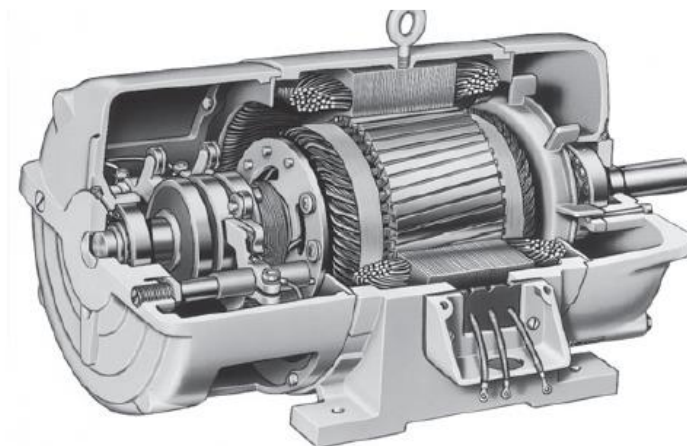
Vista em Corte de Um Motor de Indução de Rotor Bobinado. (Fonte: Chapman, 2013)
